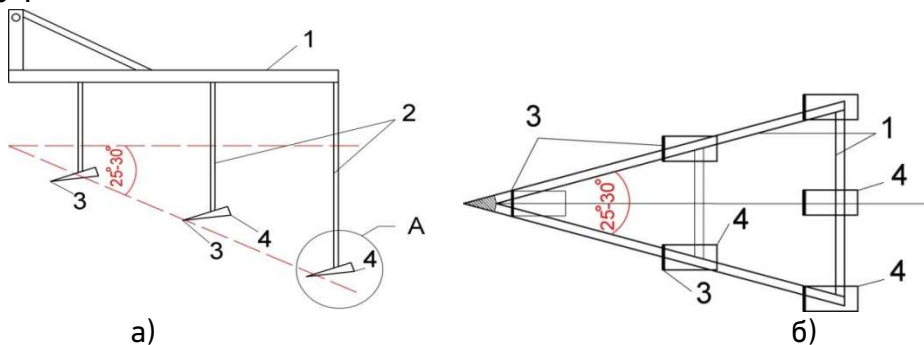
Багатоярусний розпушувач для підвищення підґрунтової фільтрації : а) – вигляд збоку; б) – вигляд зверху; А – ґрунторозробний елемент; 1 – рама; 2 – стояк; 3 – леміш; 4 – ґрунторозпушувальна поверхня
